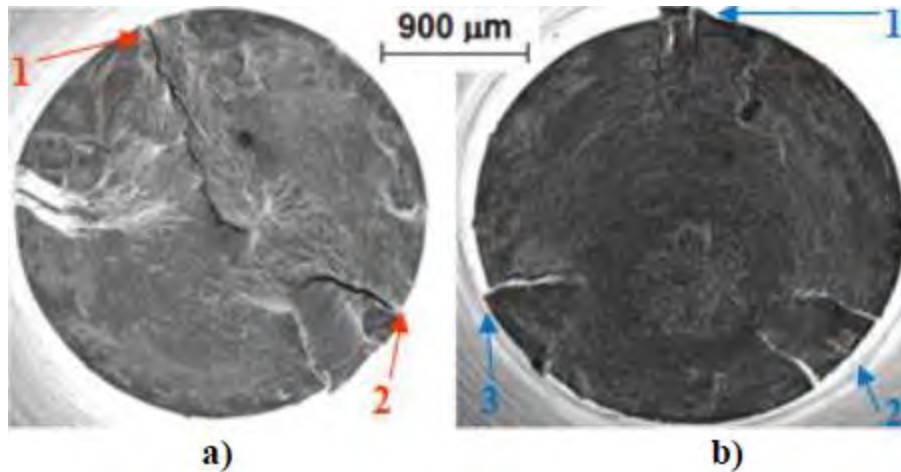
Superficies de fractura con alta carga aplicada y dos puntos de inicio de grieta a), superficies de fractura con 3 puntos de inicio de grieta que convergen en una zona granular b).
